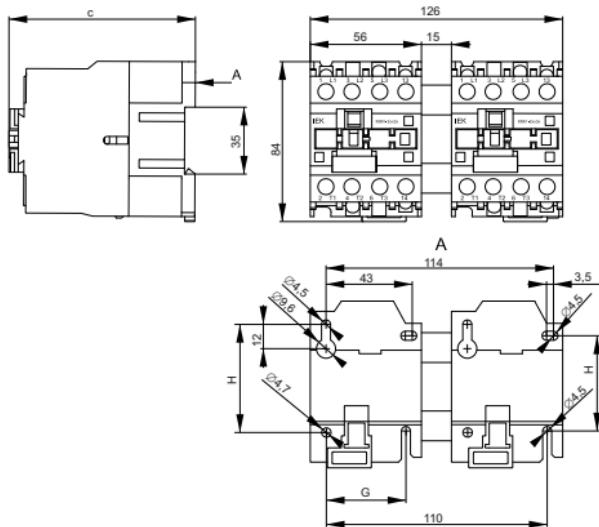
Габаритные и установочные размеры КМИ-23230, КМИ-22530 / Figure 4 – Overall and installation dimensions of KMI-23230, KMI-22530
